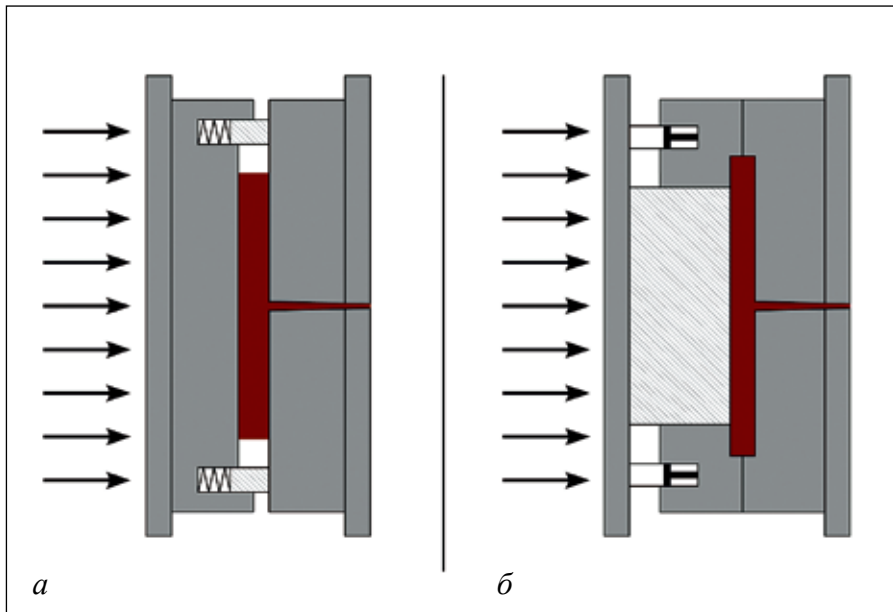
Схемы возможных вариантов исполнения литьевой формы, в которых процесс подпрессовки осуществляется с помощью узла смыкания литьевой машины (рисунок: Engel): а – подпрессовка по всей площади отливки с пружинной уплотнительной рамкой; б – подпрессовка по определенной части поверхности изделия, при которой нагрузка на уплотнительную рамку создается с помощью гидравлического устройства
